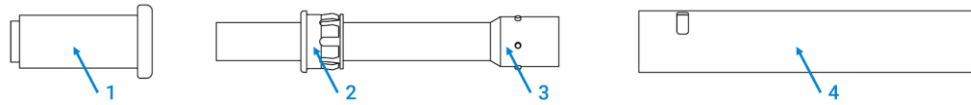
Vue illustrée de l'ensemble de tubes externes en céramique
